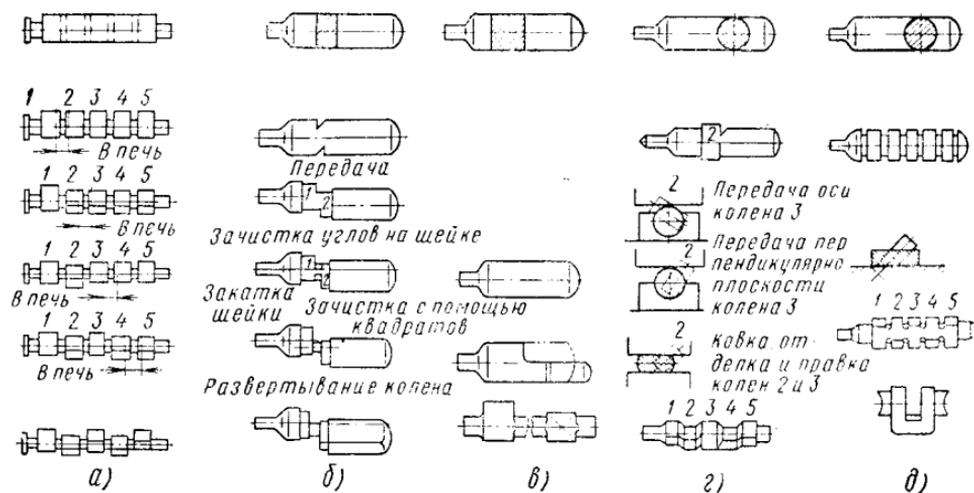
Способыковки коленчатых валов (1—5 — номера колен)
